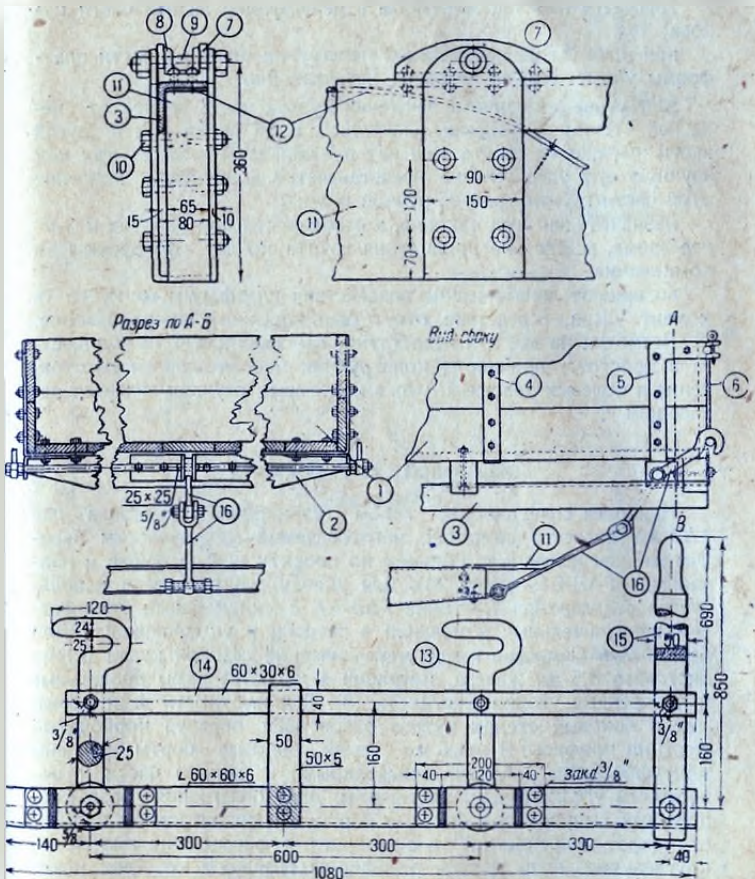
Общая схема шарнирного самосвала сист. Румянцева.
